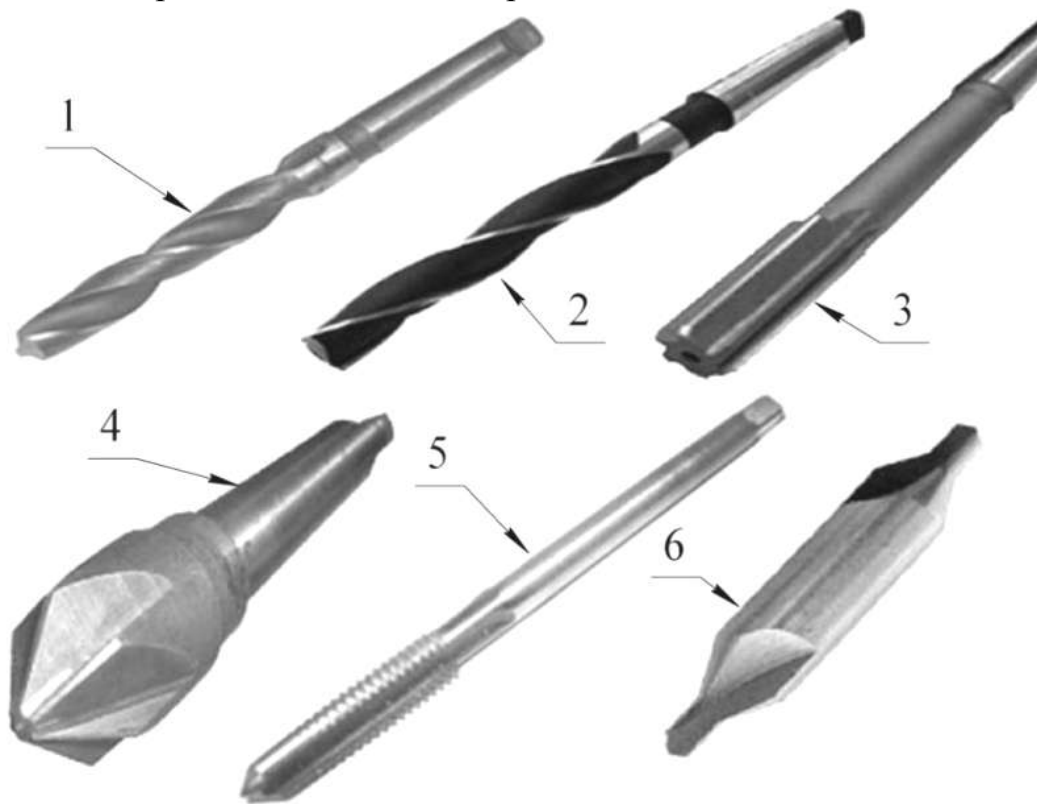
Різальні інструменти, що використовують на верстатах свердильно-розточувальної групи:
